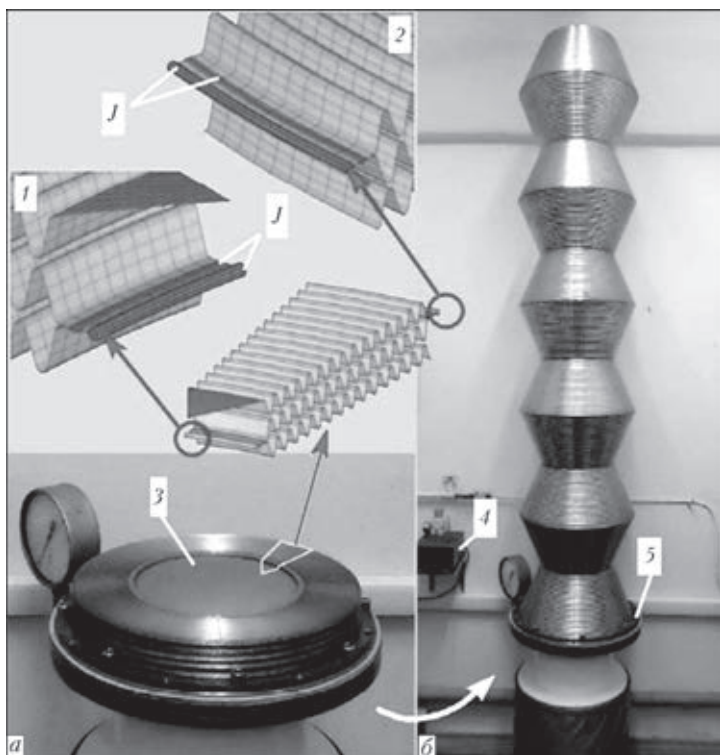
Коническая КПО из одиннадцати оболочек в компактном (а) и раскрытом (б) положениях. Слева сверху — модели сегментов конструкции с внутренним (1) и наружным (2) кольцевыми сварными соединениями J (3 — замыкающий элемент; 4 — компактный компрессор с мановакуумметром; 5 — жесткий вакуумплотный контур стенда раскрытия)
